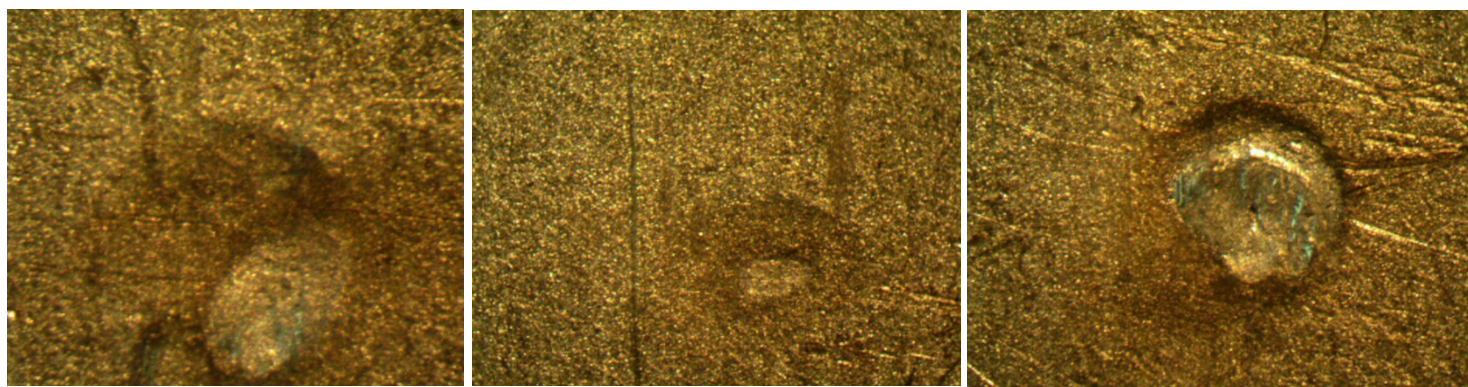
Места точечной сварки в месте отрыва под микроскопом
